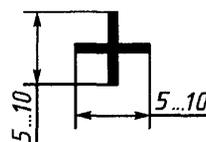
Обозначение видимой одиночной сварной точки
